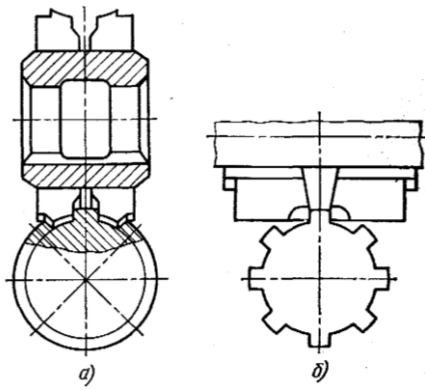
Схема фрезерування шліців фасонними фрезами:
